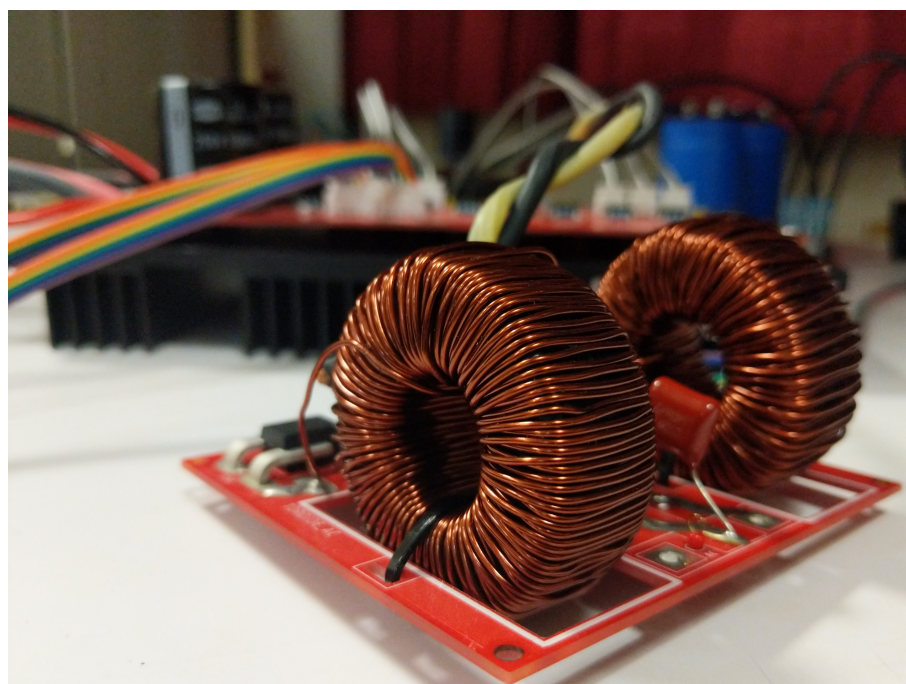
PCB del filtro LCL fabricado ya ensamblado.
